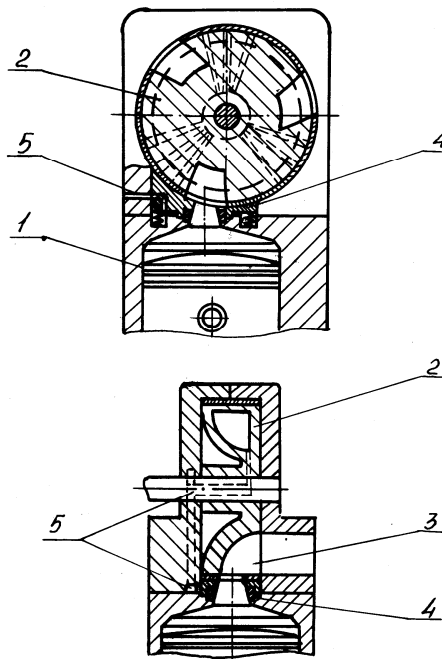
Газораспределительный механизм с цилиндрическим золотником: 1 — цилиндр; 2 — цилиндрический золотник; 3 — каналы; 4 — система уплотнений; 5 — каналы для охлаждения
